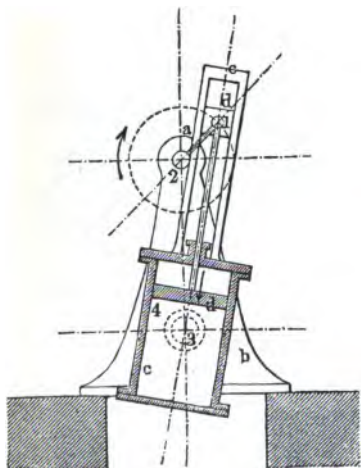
Machine oscillante; le lien b étant fixe, les pièces coulissantes c et d oscillent autour de l'articulation fixe 3 (d'après Reuleaux).
